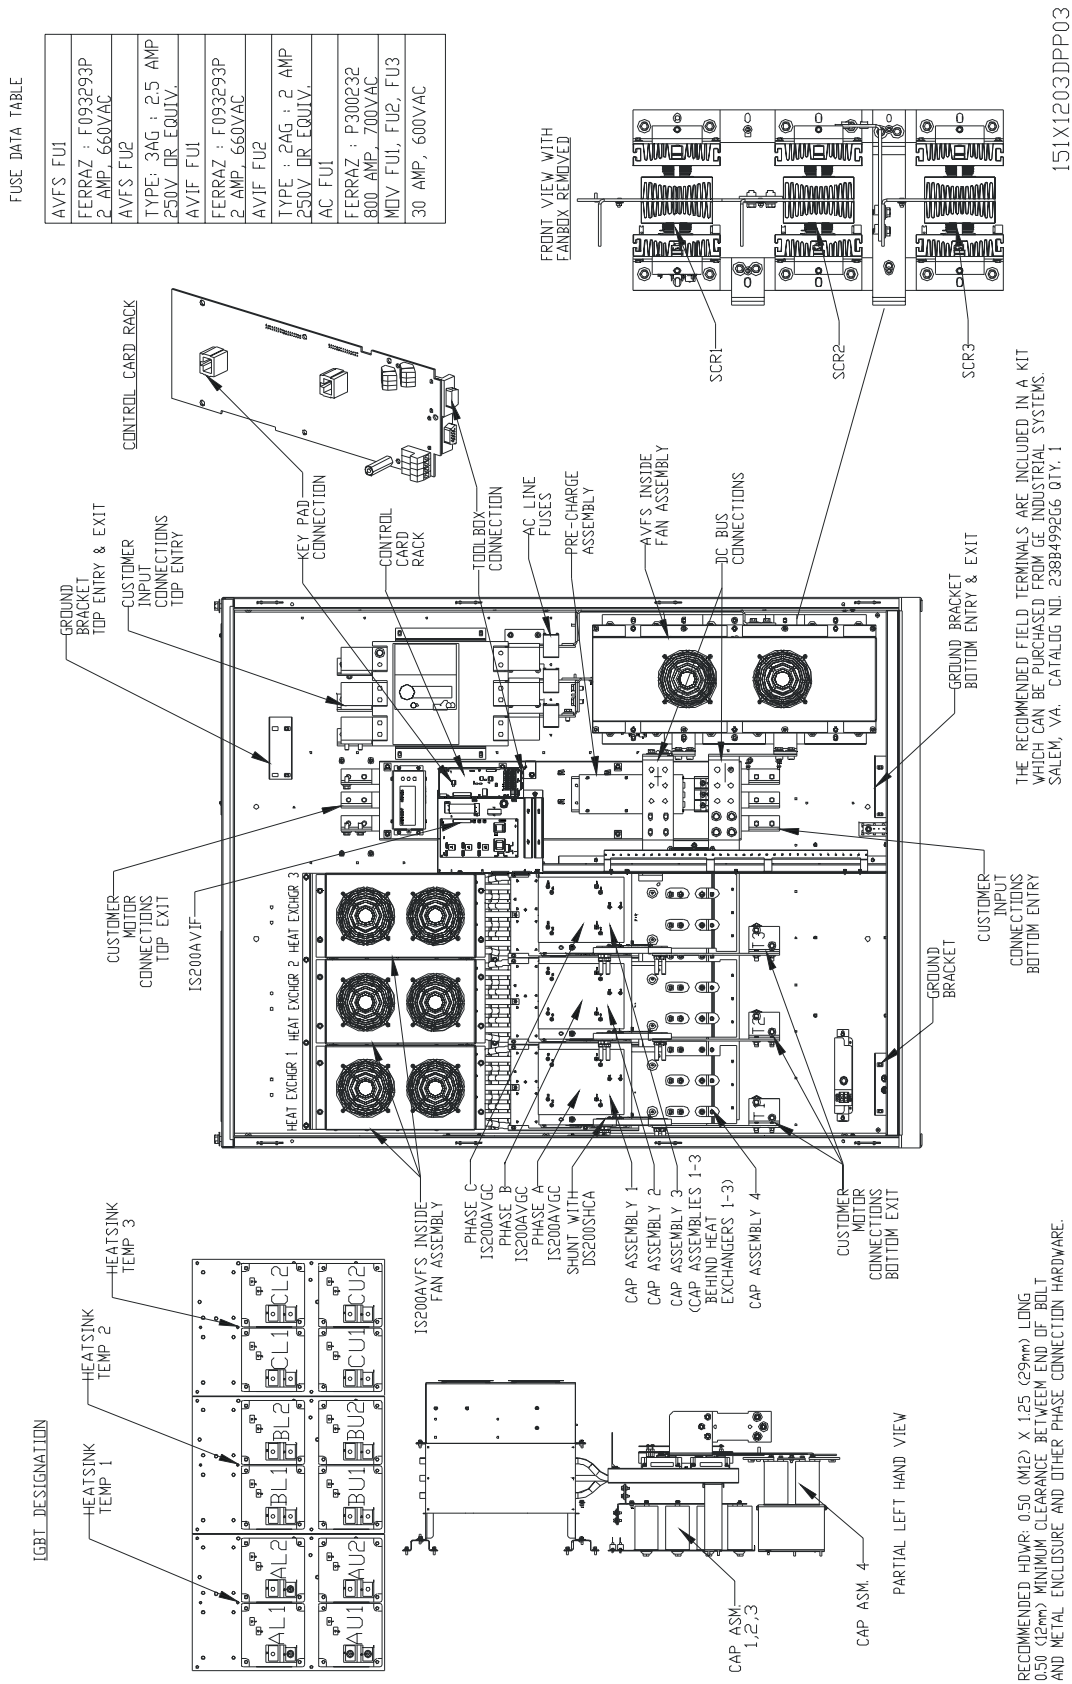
Габаритный чертеж 500 - 800 Лс.
